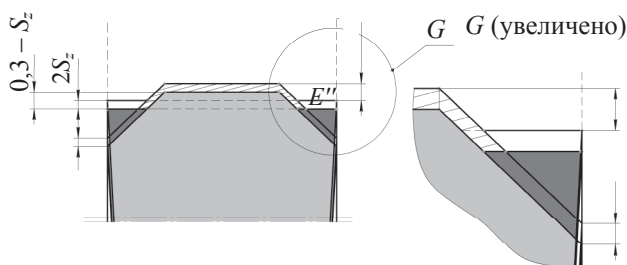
Схема формирования пропила дисковой твердосплавной пилой с плоско-трапециевидным профилем зубьев
